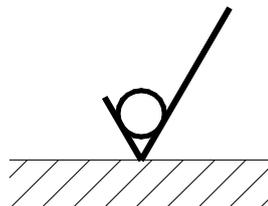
símbolo de estado de superfície que não permite retirada de material.
